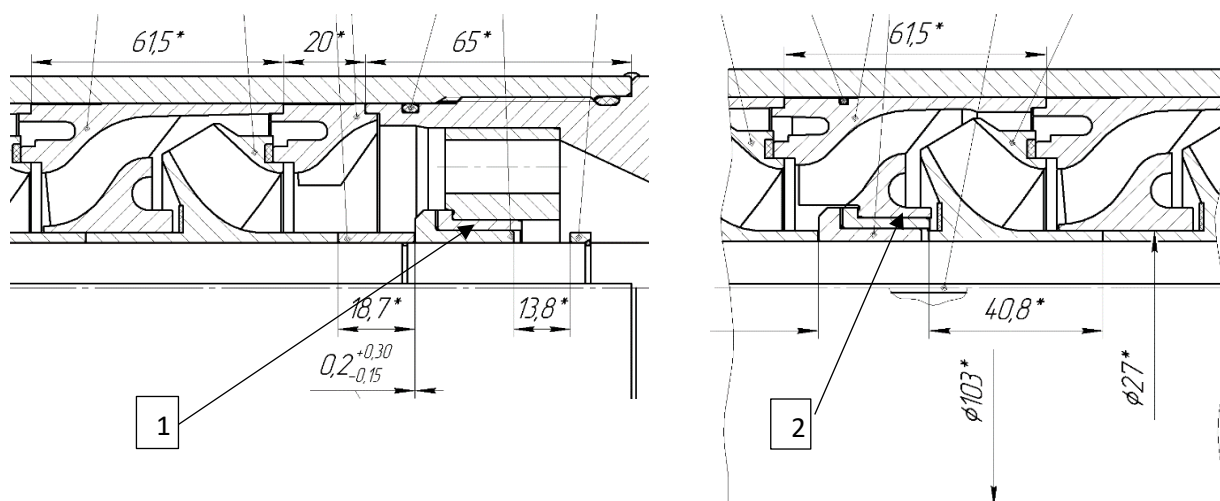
детали ступени 5А-500 (1 – концевой подшипник, 2 – промежуточный подшипник)
